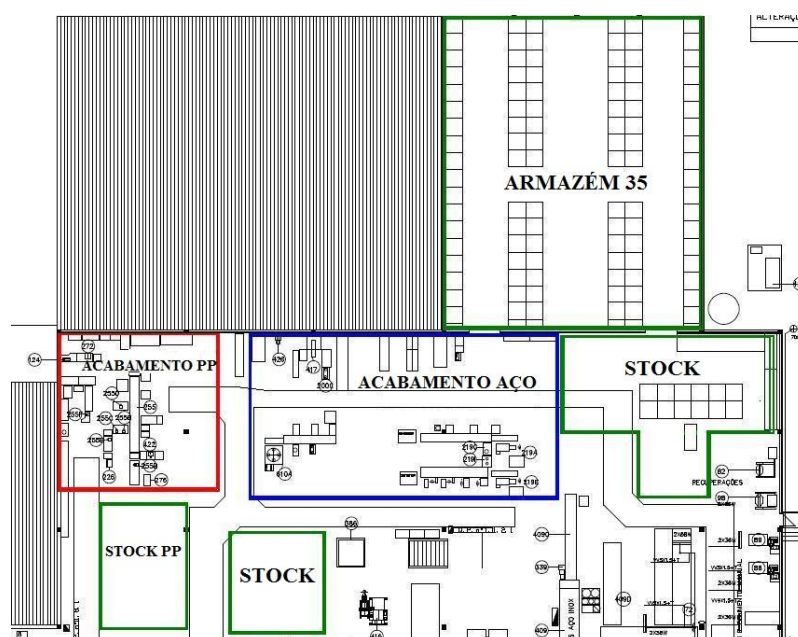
Layout Acabamento* (Adaptado de documento interno da Silampos)
